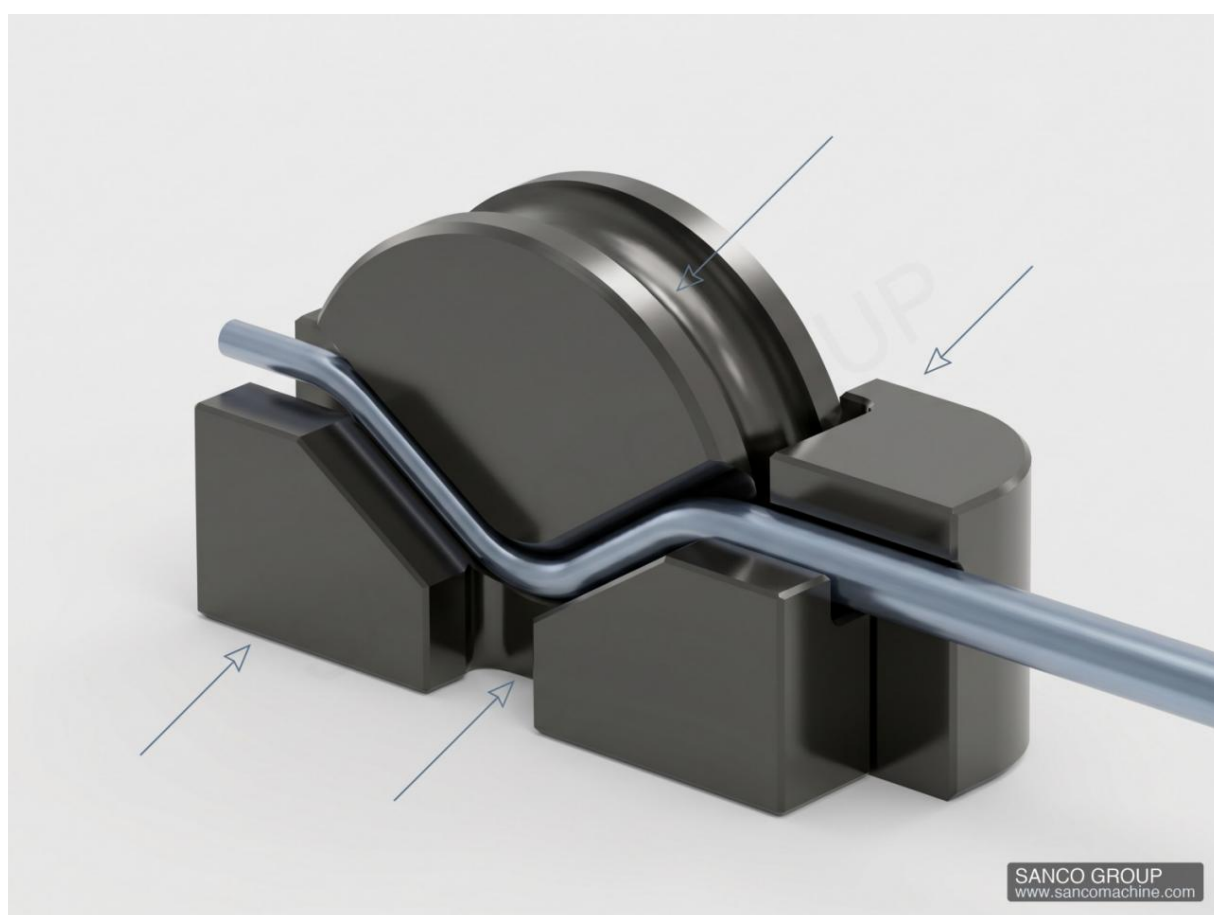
Рендер разреза гибочной матрицы из твердого сплава C12 (включая комплект из гибочной, зажимной и прижимной матриц) — —© SANCO GROUP · www.sancomachine.com
